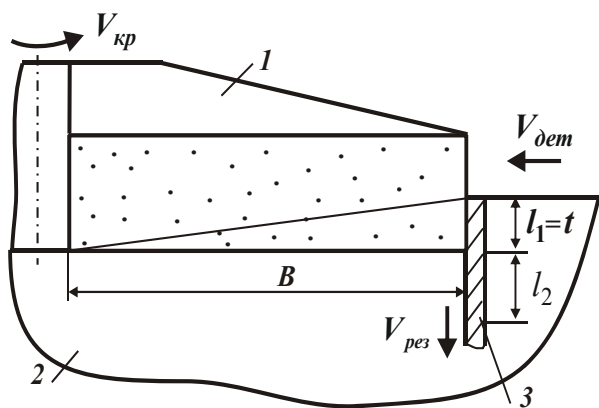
Расчетная схема торцового шлифования: 1 – круг; 2 – обрабатываемый материал; 3 – адиабатический стержень
